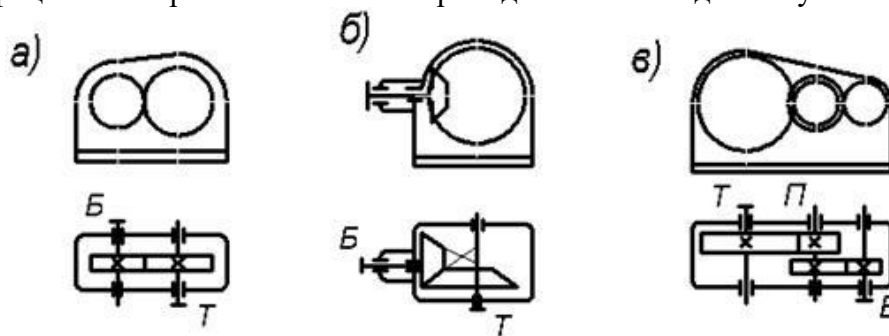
Кинематические схемы зубчатых редукторов
